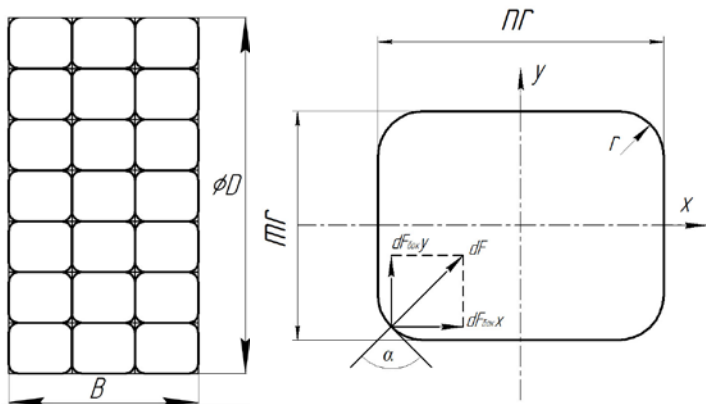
Рабочая поверхность банджа валка с наплавленной футерующей сеткой:
